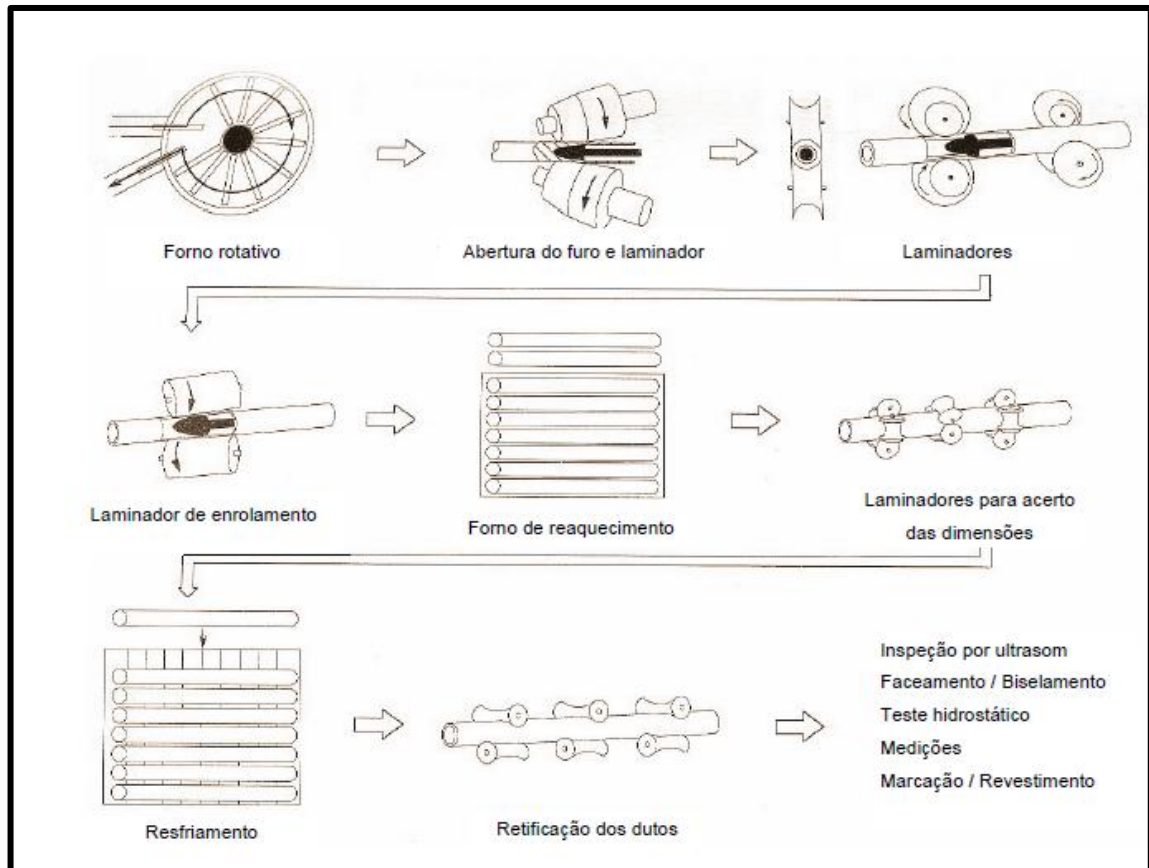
Processo de fabricação de tubos por extrusão (modificada) [3].
